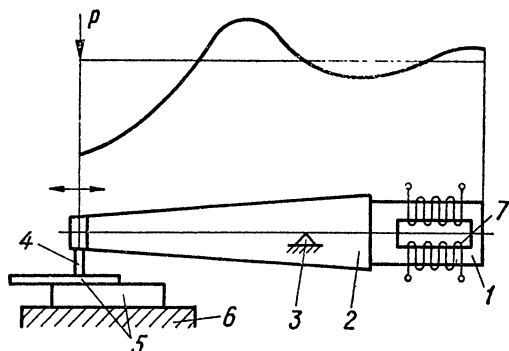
Схема ультразвуковой сварки металлов продольными колебаниями
